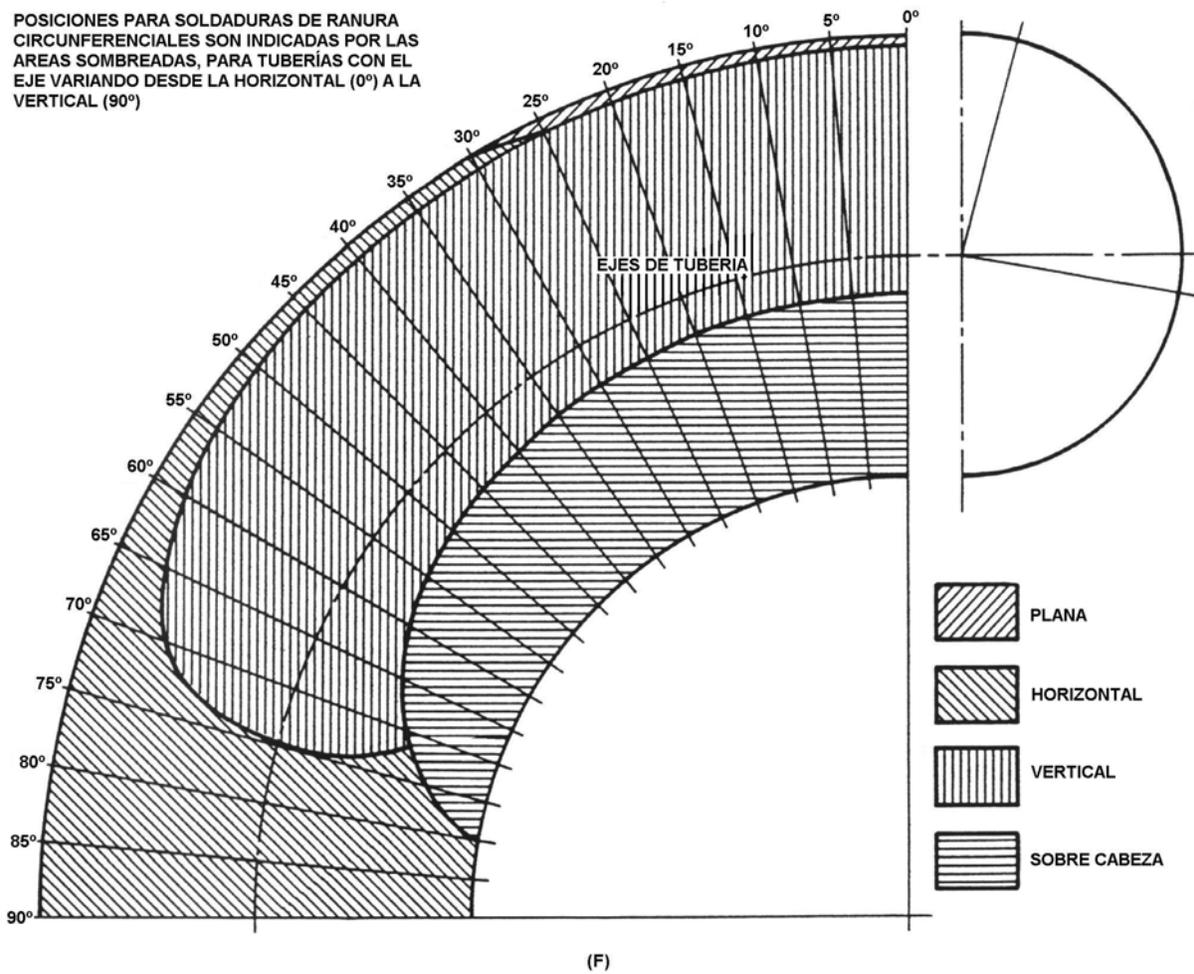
C - Diagrama de Posición de Soldadura para Soldaduras de Ranura en Tubería
